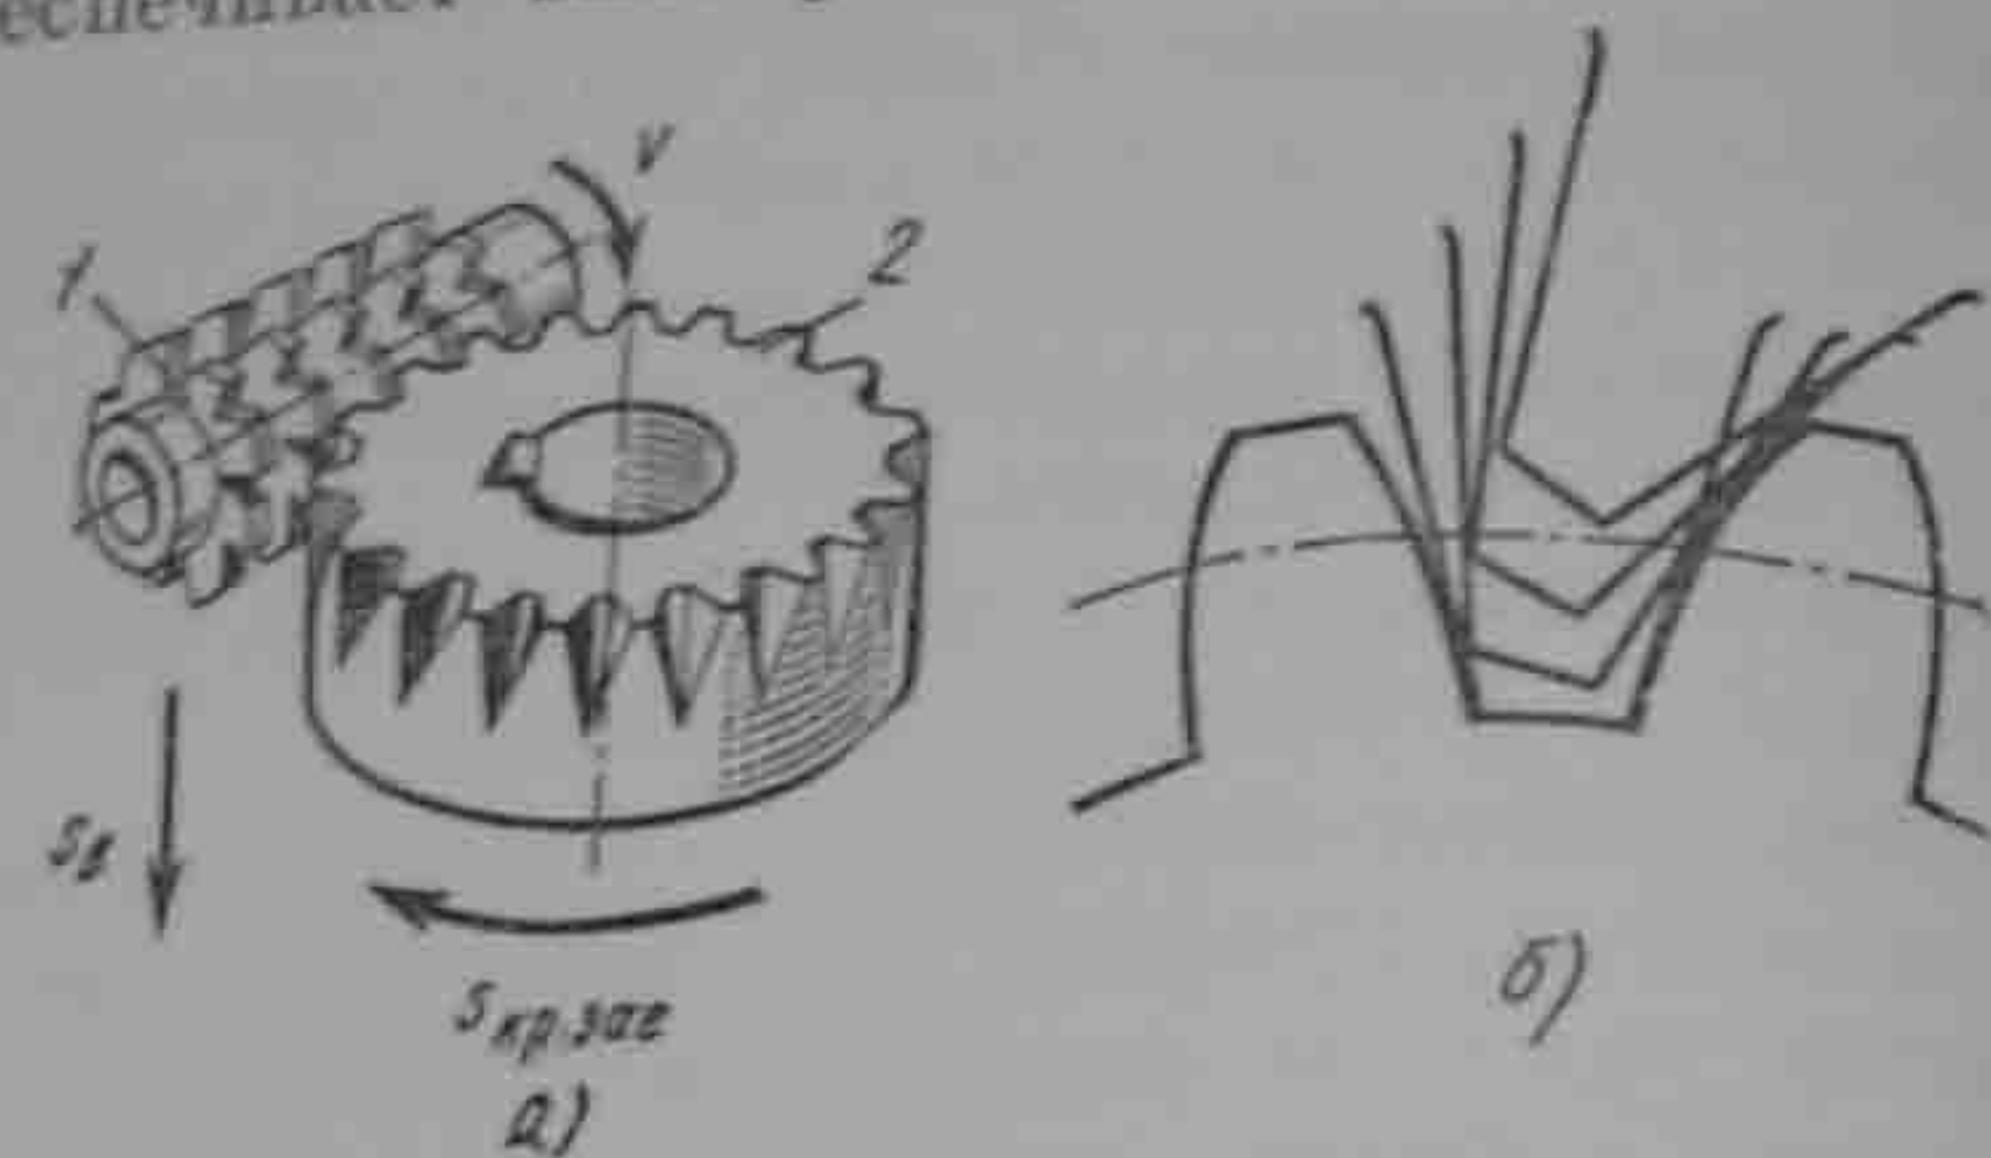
Схема формообразования зубьев цилиндрического колеса червячной модульной фрезой:
